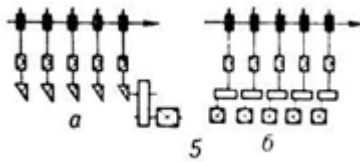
Схема расположения рабочих клеток прокатного стана 5 — непрерывного (а — с групповым приводом, б — с индивидуальным)
